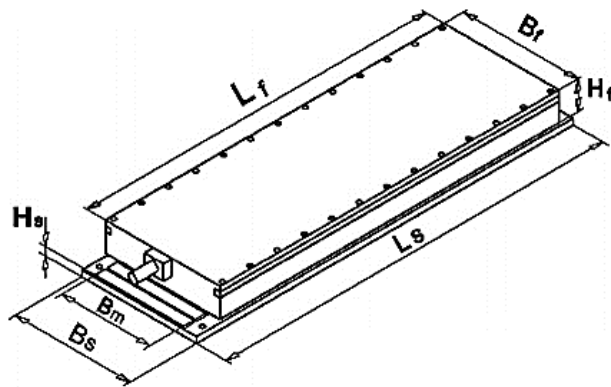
Основные размеры якоря и индуктора двигателя LSM-36
